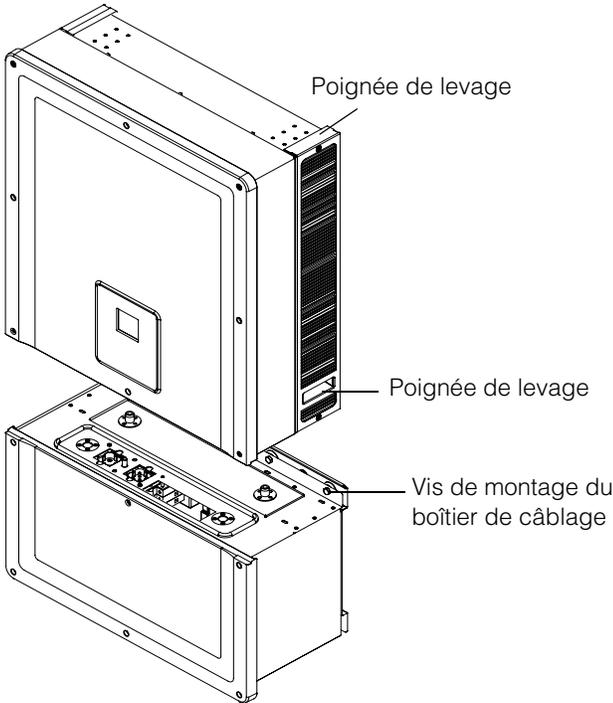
Onduleur et boîtier de câblage – Vue éclatée
